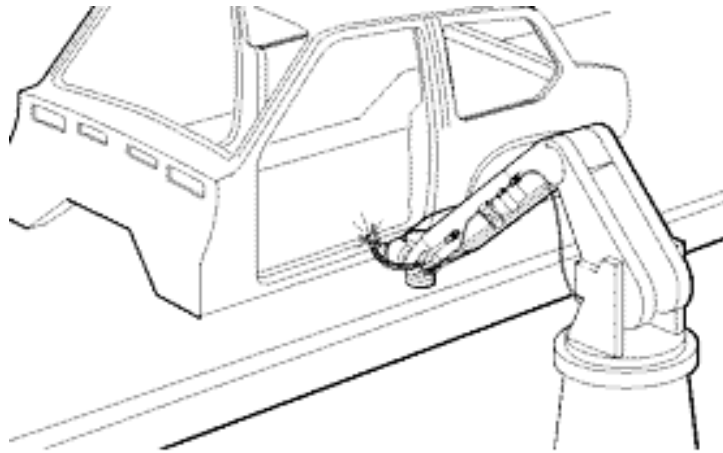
Robot soldador de carrocerías utilizando un chorro de aire frío directamente en el punto de contacto.
